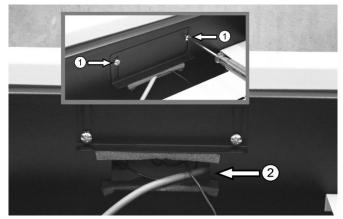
Cable de 2 en la caja de la caja del interruptor
